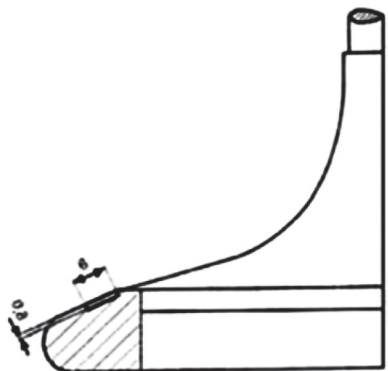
Торцевая поверхность тарелки клапана для лазерной порошковой наплавки
